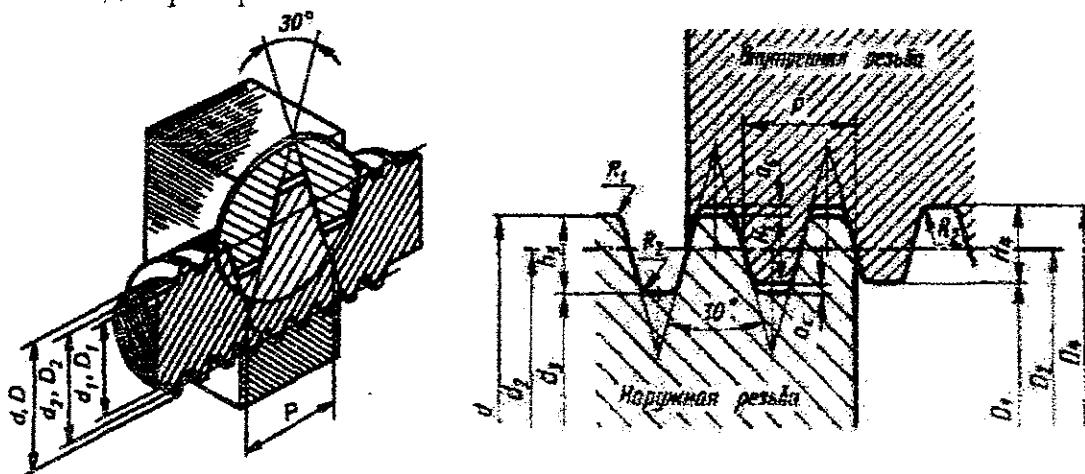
Профиль и основные размеры трапециoidalной резьбы
